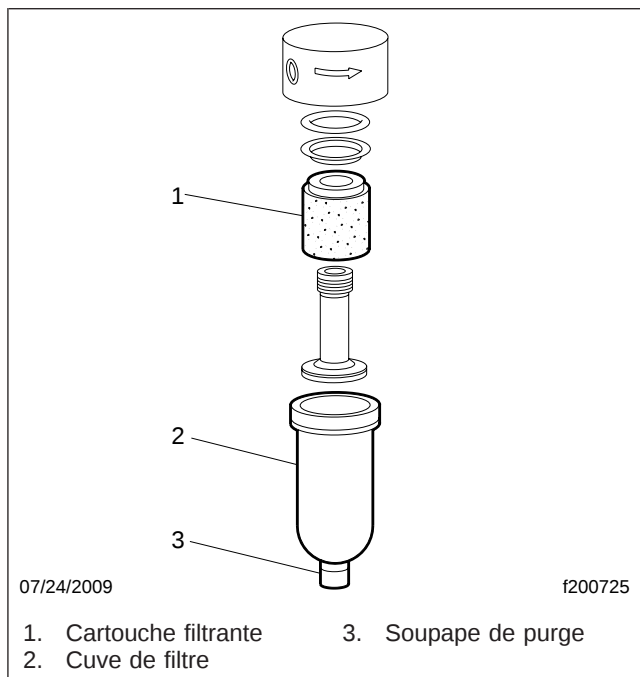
, Filtre à air d'électrovalve Horton DriveMaster
